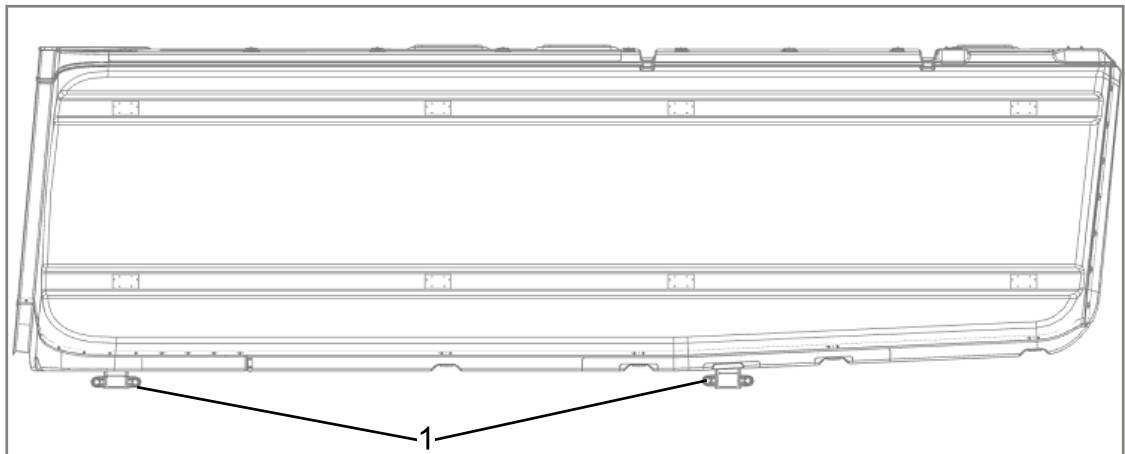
Maschinenhaus, Ansicht seitlich mit Transportfüßen (1)
